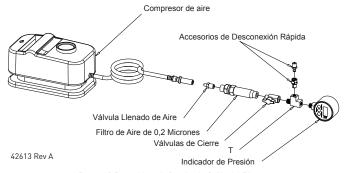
Ensamblaje de Prueba de Caída del Técnico
